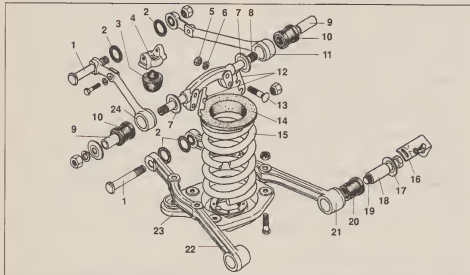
Элементы передней подвески: 1 – пальцы; 2 – уплотнительные кольца; 3 – буфер хода отдачи; 4 – опора буфера верхних рычагов; 5, 6, 13 – гайка, шайба и болт крепления балки передней подвески к кузову; 7 – шайбы; 8 – ось верхних рычагов; 9 – распорные втулки; 10 – резиновые втулки шарниров верхних рычагов; 11, 24 – верхний задний и верхний передний рычаги; 12 – регулировочные прокладки; 14 – прокладка пружины; 15 – пружина; 16 – регулировочная прокладка нижних рычагов; 17 – шайба; 18 – распорная втулка; 19 – пальцы; 20 – резиновая втулка нижнего рычага; 21, 22 – нижний задний и нижний передний рычаги; 23 – чашка пружины с усилителями.
